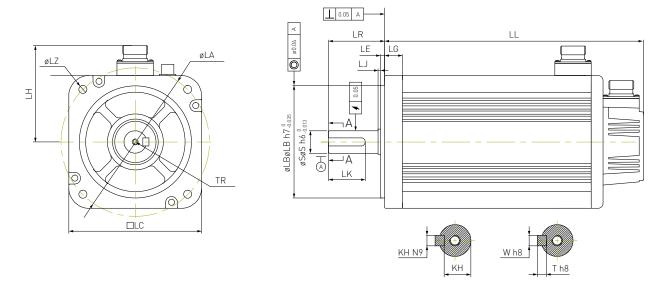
Габаритные размеры серводвигателя ELM1H-xxx (220VAC).
